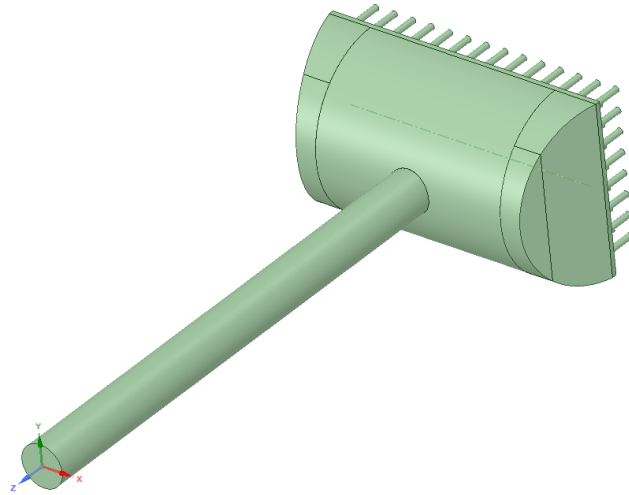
Desenho técnico da seção de testes (com retificador).
